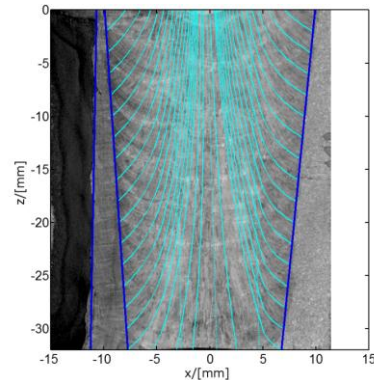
Schlibbild einer Mischnaht mit Pufferung und Schweißnahtmodell
